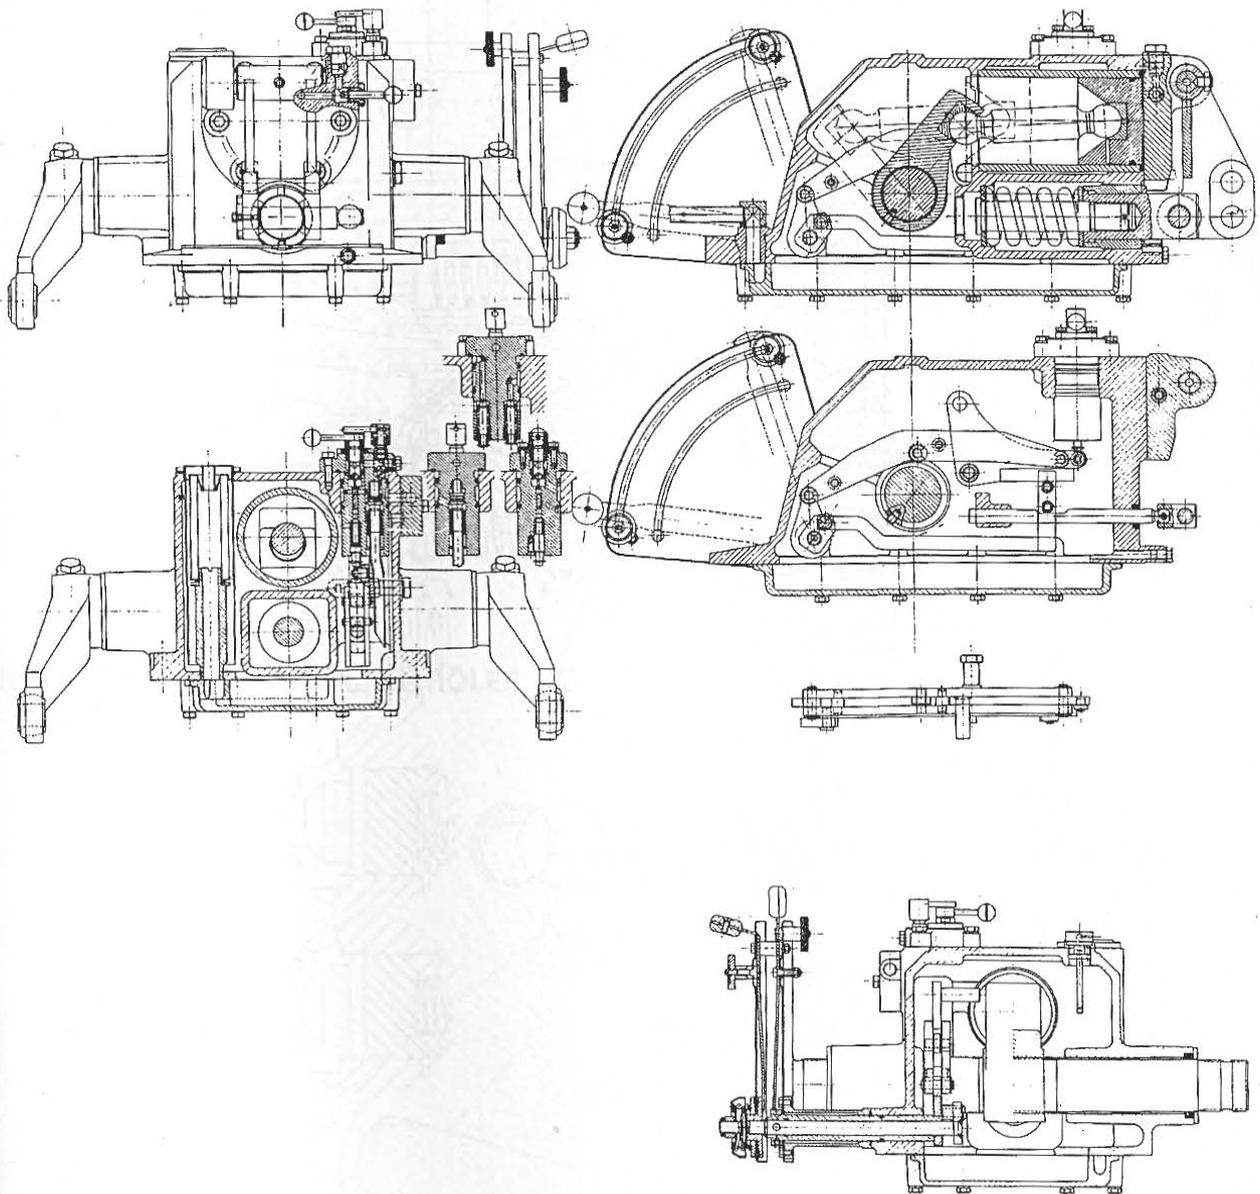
Vue d'ensemble du dispositif de relevage hydraulique
